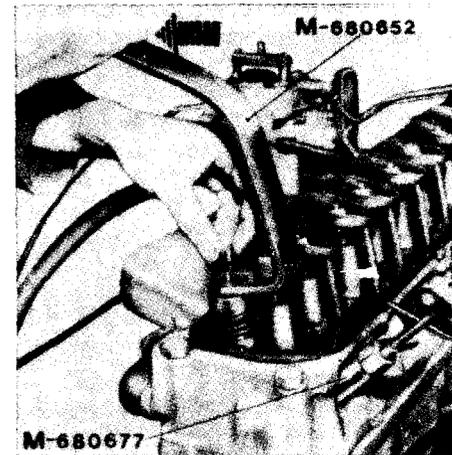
E — Remoção ou instalação da chaveta da válvula
